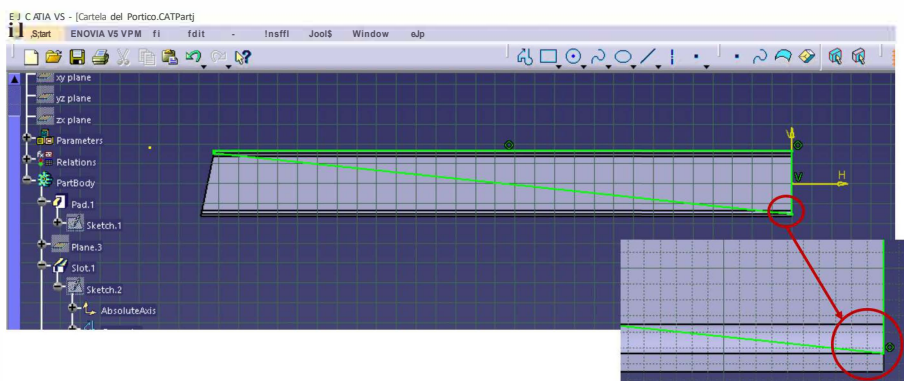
Sketch de la segunda sección de corte de la cartela
